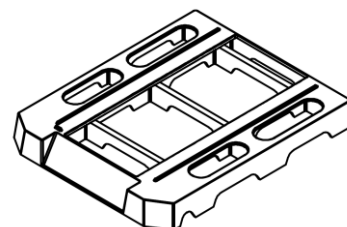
Gusseiserner Sockel für den Kessel
